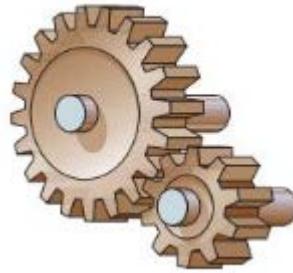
Pareja de engranajes. Fuente Libro 3º E.S.O. Ed: Oxford
